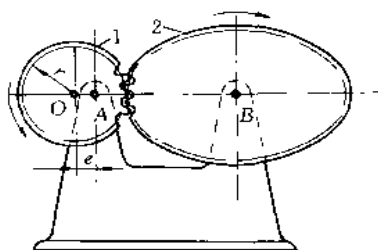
偏心圆齿轮-二叶卵圆齿轮机构
